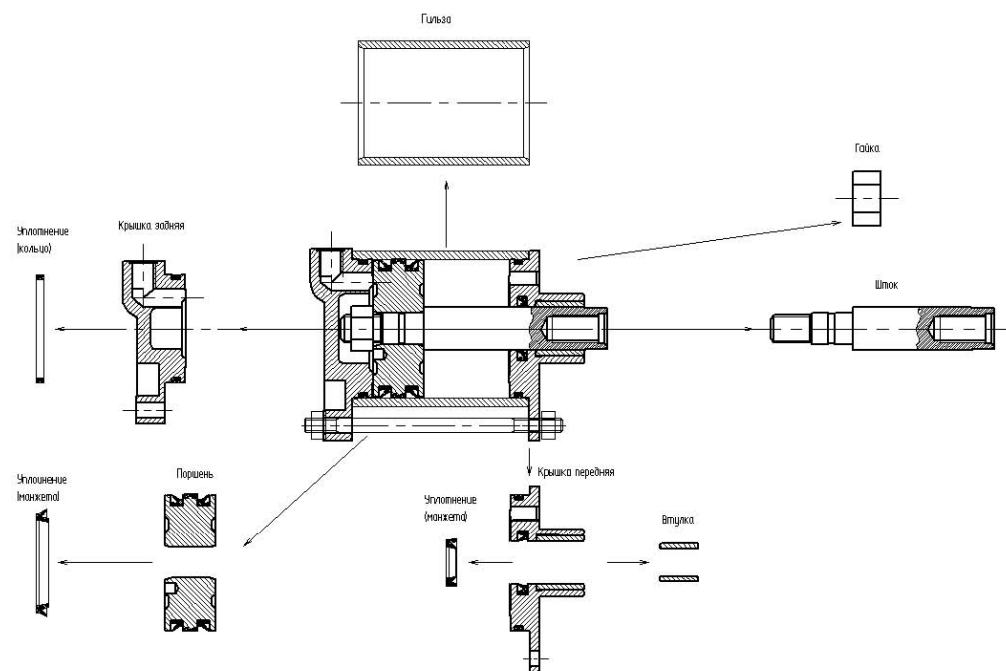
«Взрывная» схема двухстороннего пневматического цилиндра
